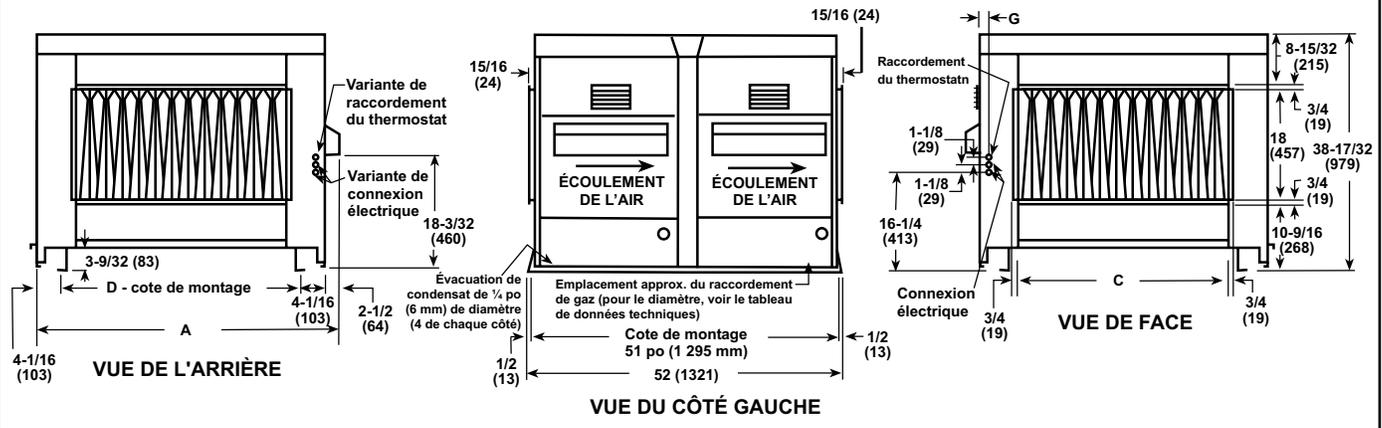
A - Dimensions, modèle série RP - pouces ± 1/8 / mm ±3
